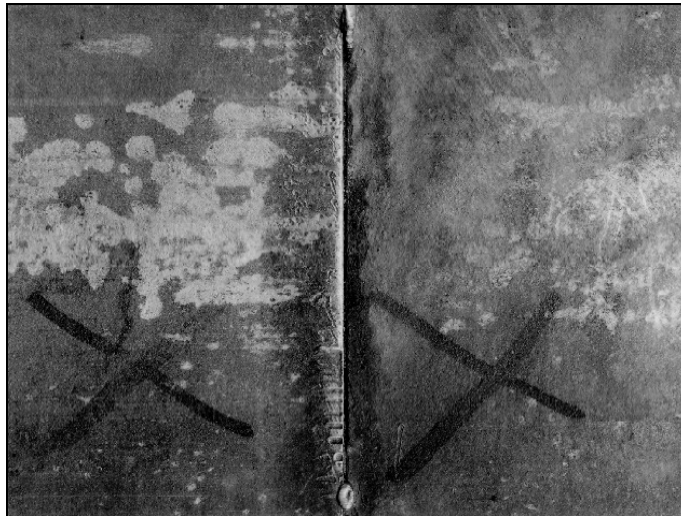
Fractura ocasionada por combinación de soldadura defectuosa y fatiga
